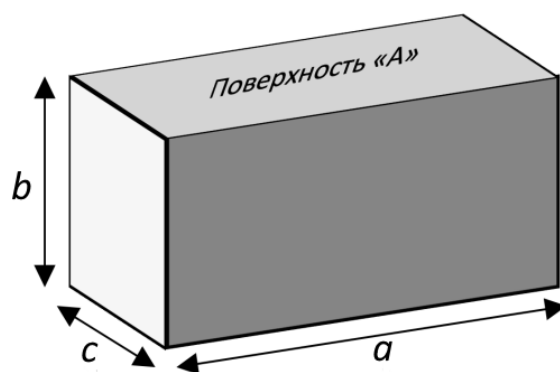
Форма и размеры исследуемых образцов из стали 40X
